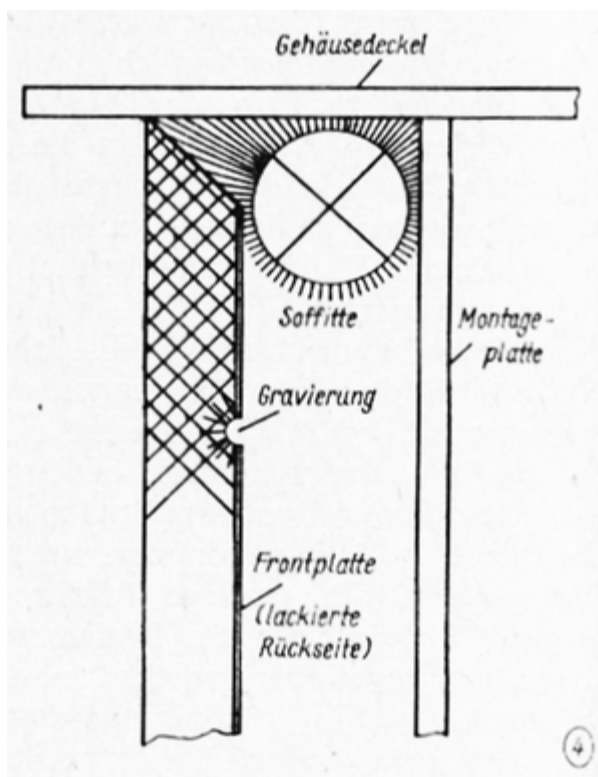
Prinzip der inneren Frontplattenbeleuchtung
